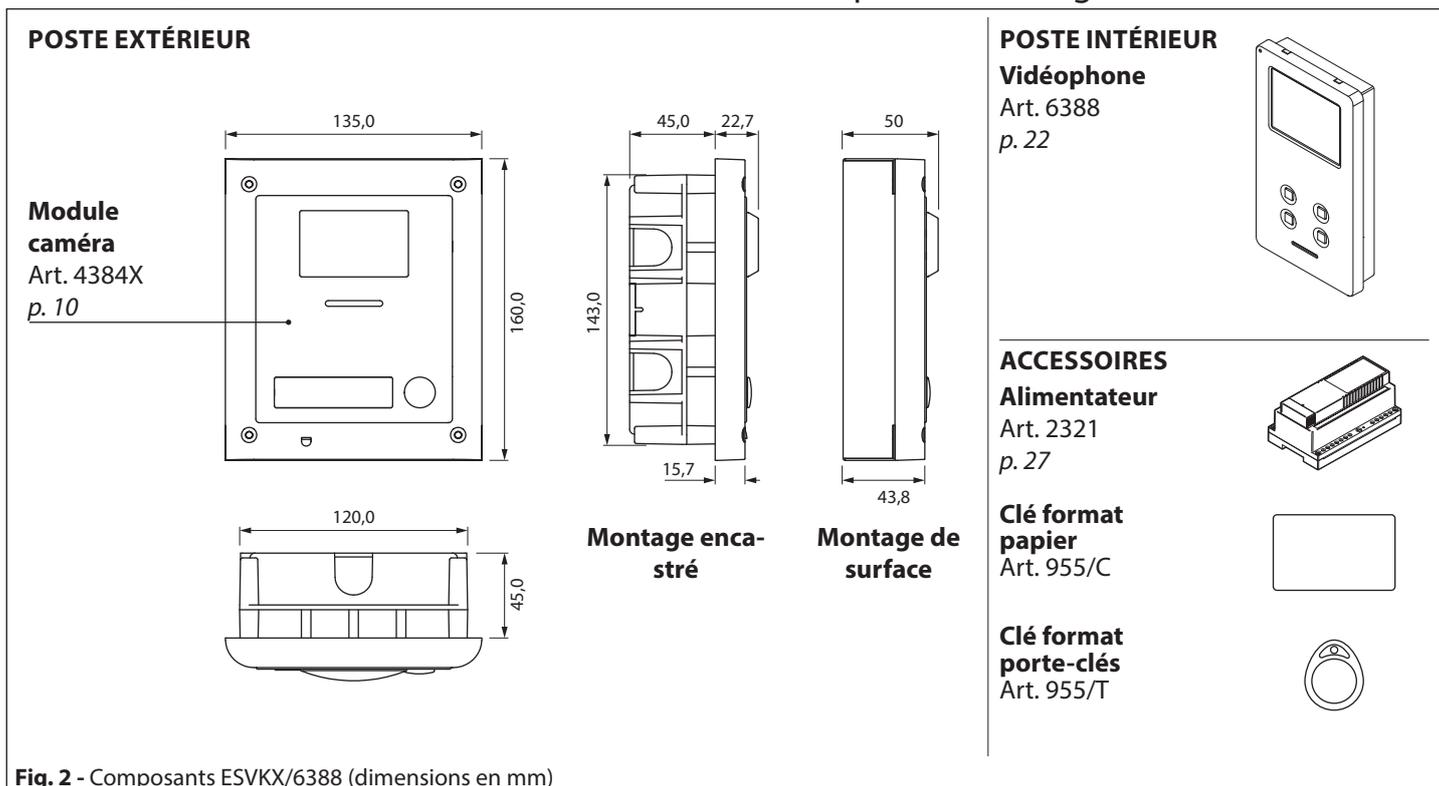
Composants ESVKX/6388 (dimensions en mm)
